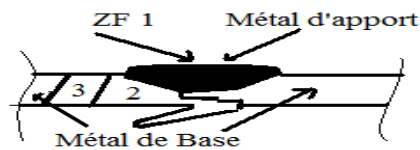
Mode d'assemblage du joint soudé des deux embouts du corps de la bouteille à gaz.
